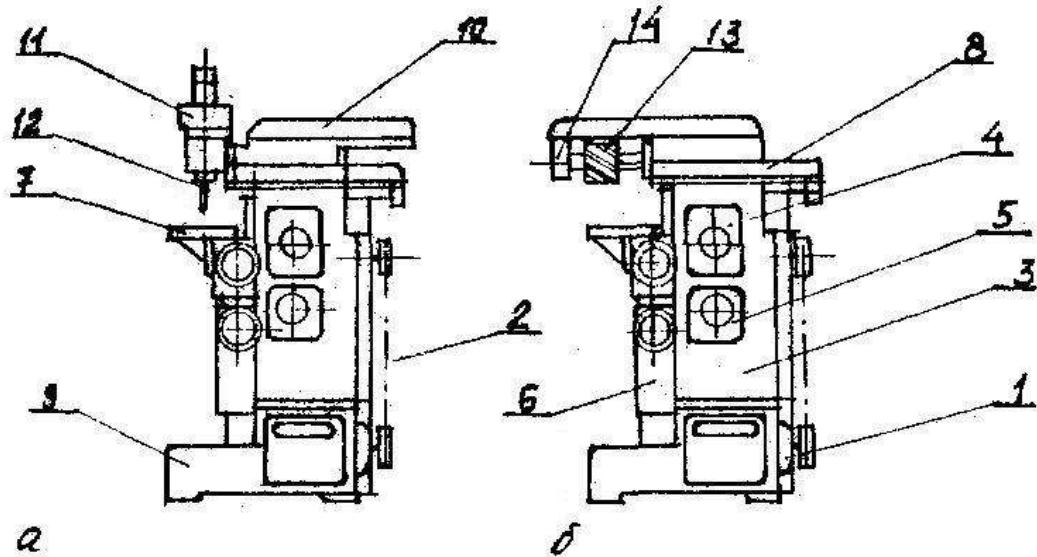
Основні вузли широкоуніверсального фрезерувального верстата
